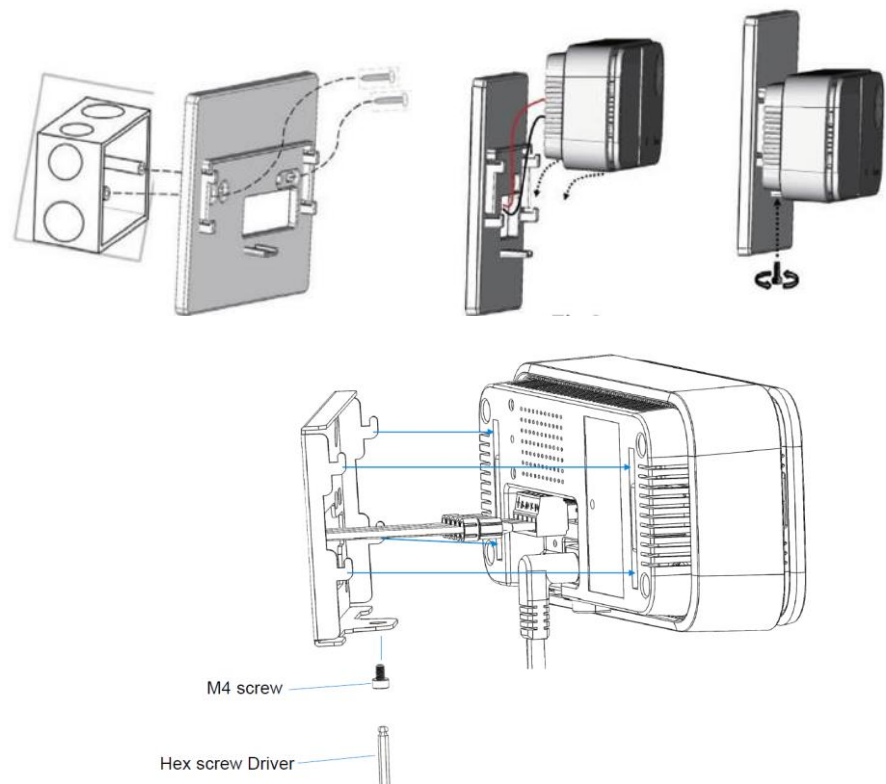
Montage an 4 Haken und Fixierung mit M4-Schraube.
